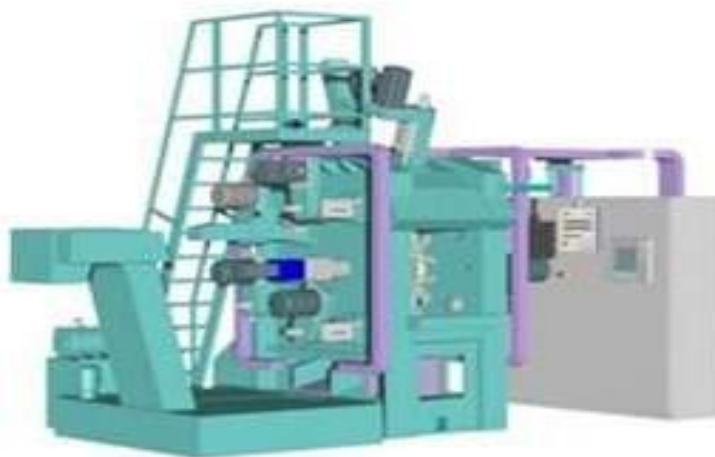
Компонування агрегатного верстата з поворотним барабаном VIGNOTTO Vi03
